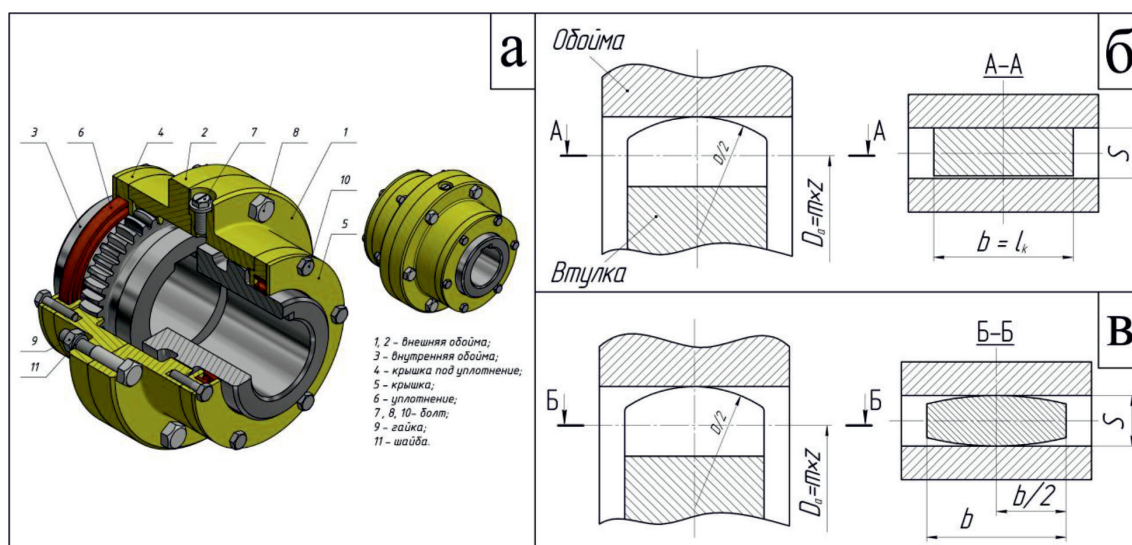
Общий вид и устройство зубчатой муфты (а), форма зубьев втулки с линейными (б) и криволинейными образующими (бочкообразные зубья) (в)
